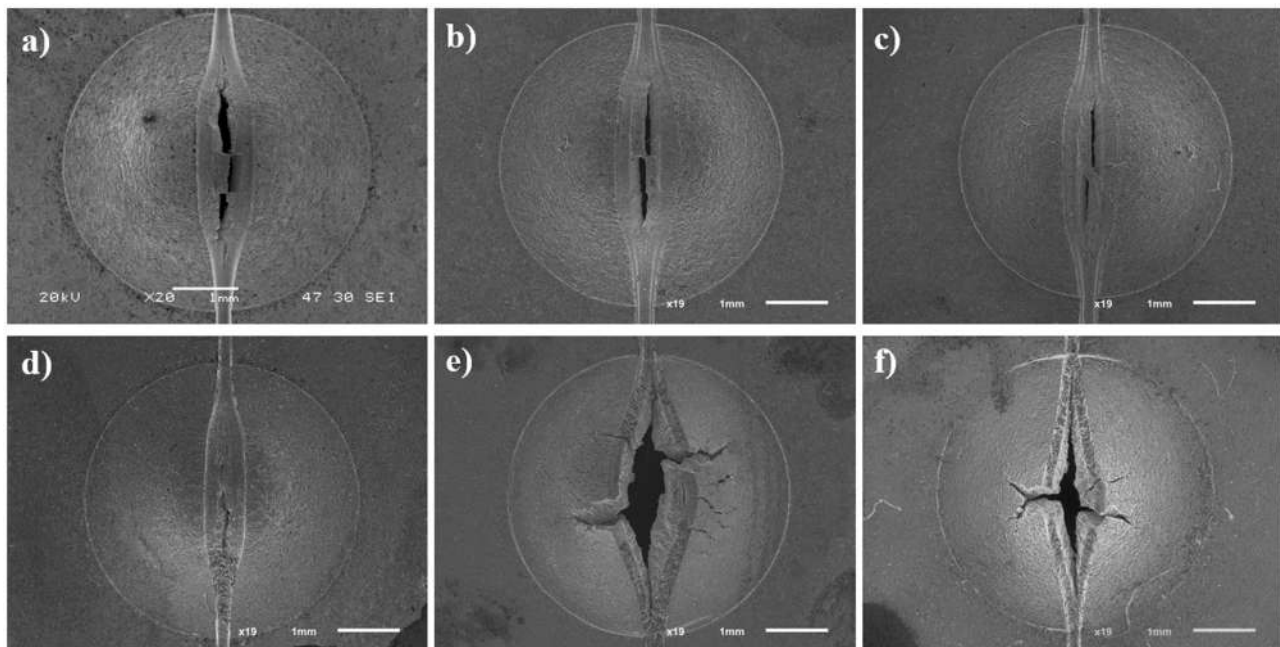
Fractografías SPT. a) Metal base; b) ZAT; c) Material soldado; d) Metal base precargado; e) ZAT precargado; f) Material soldado pre-cargado
